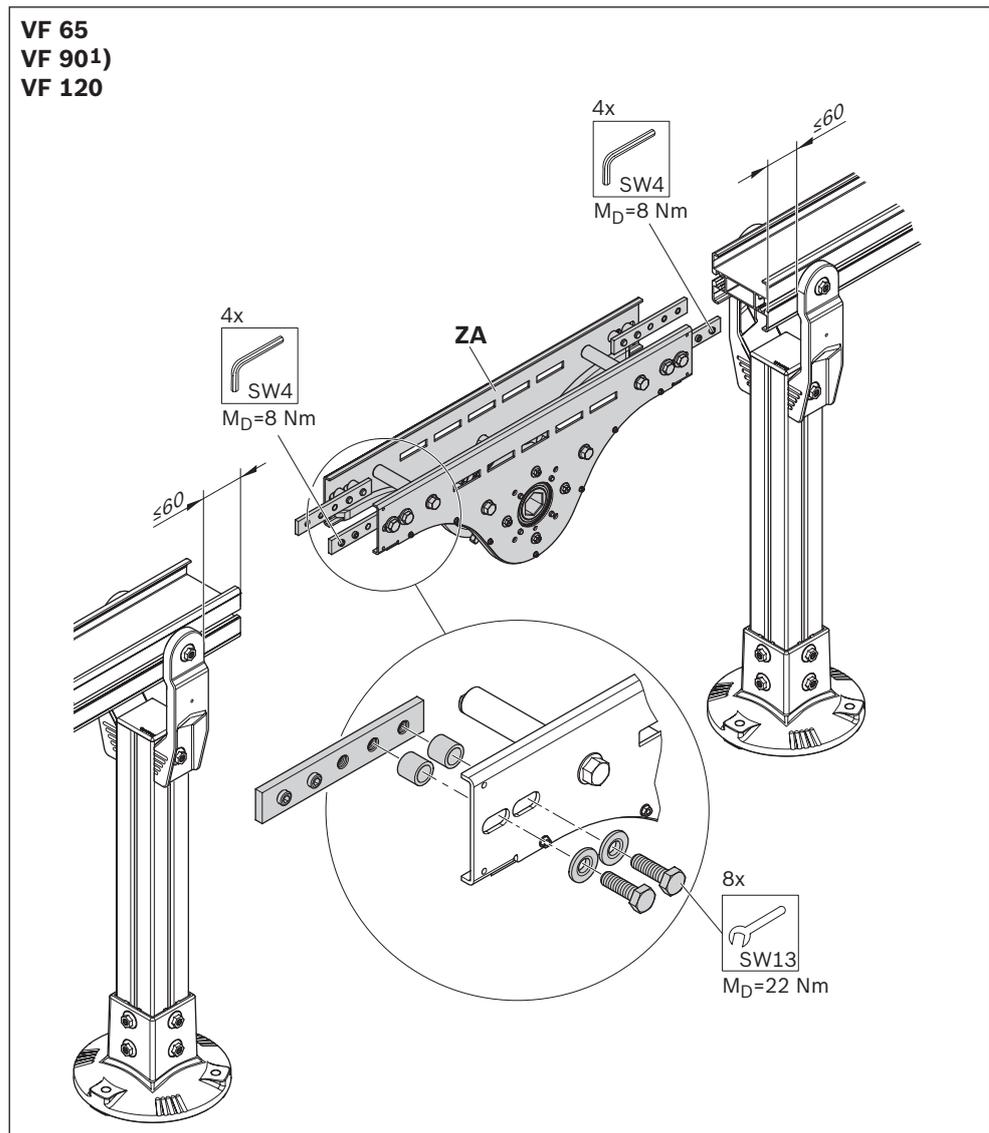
Sistema AL, montaggio dell'azionamento centrale
